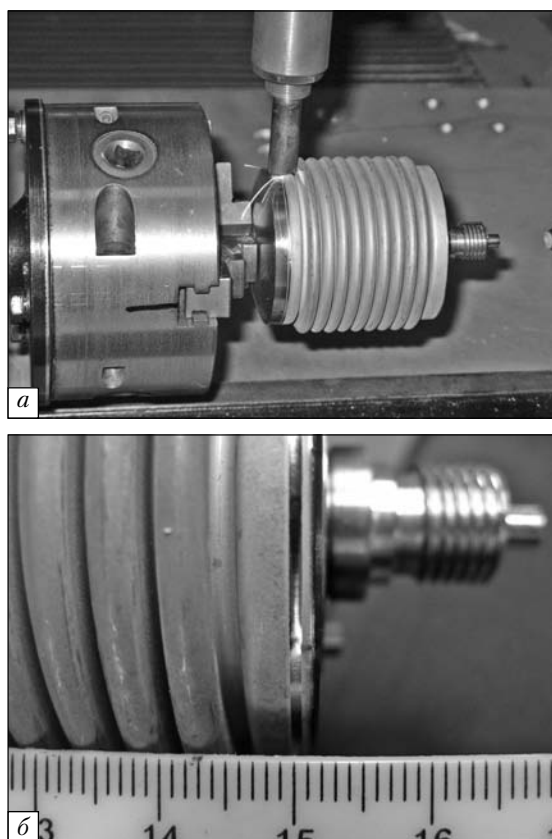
Процес лазерного зварювання сильфонного компенсуючого елемента (*a*) і зовнішній вигляд одержаного зварного шва (*b*)
